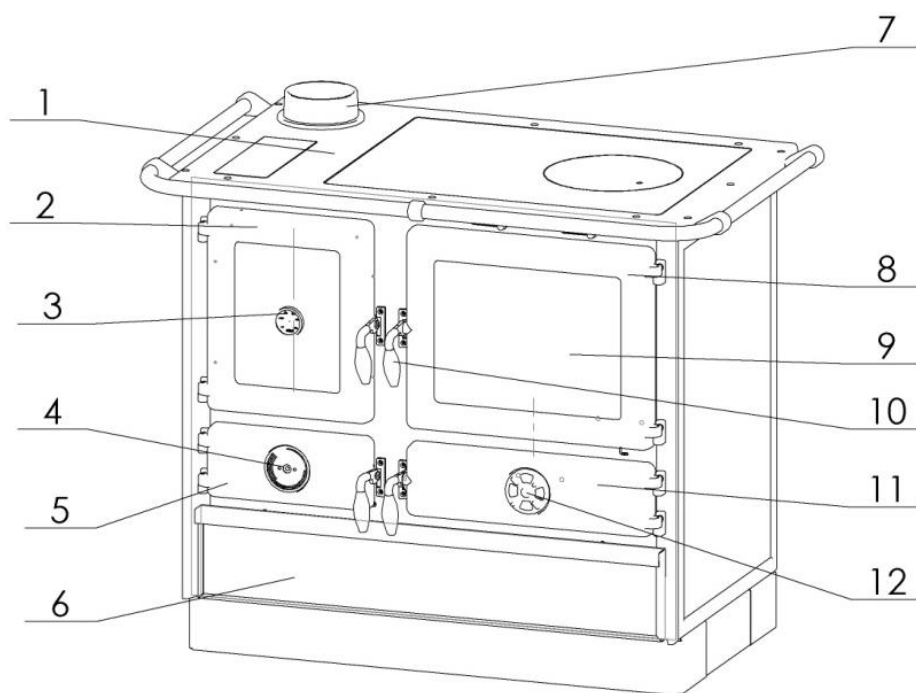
Integralne części kuchenki Super Thermo Magnum
